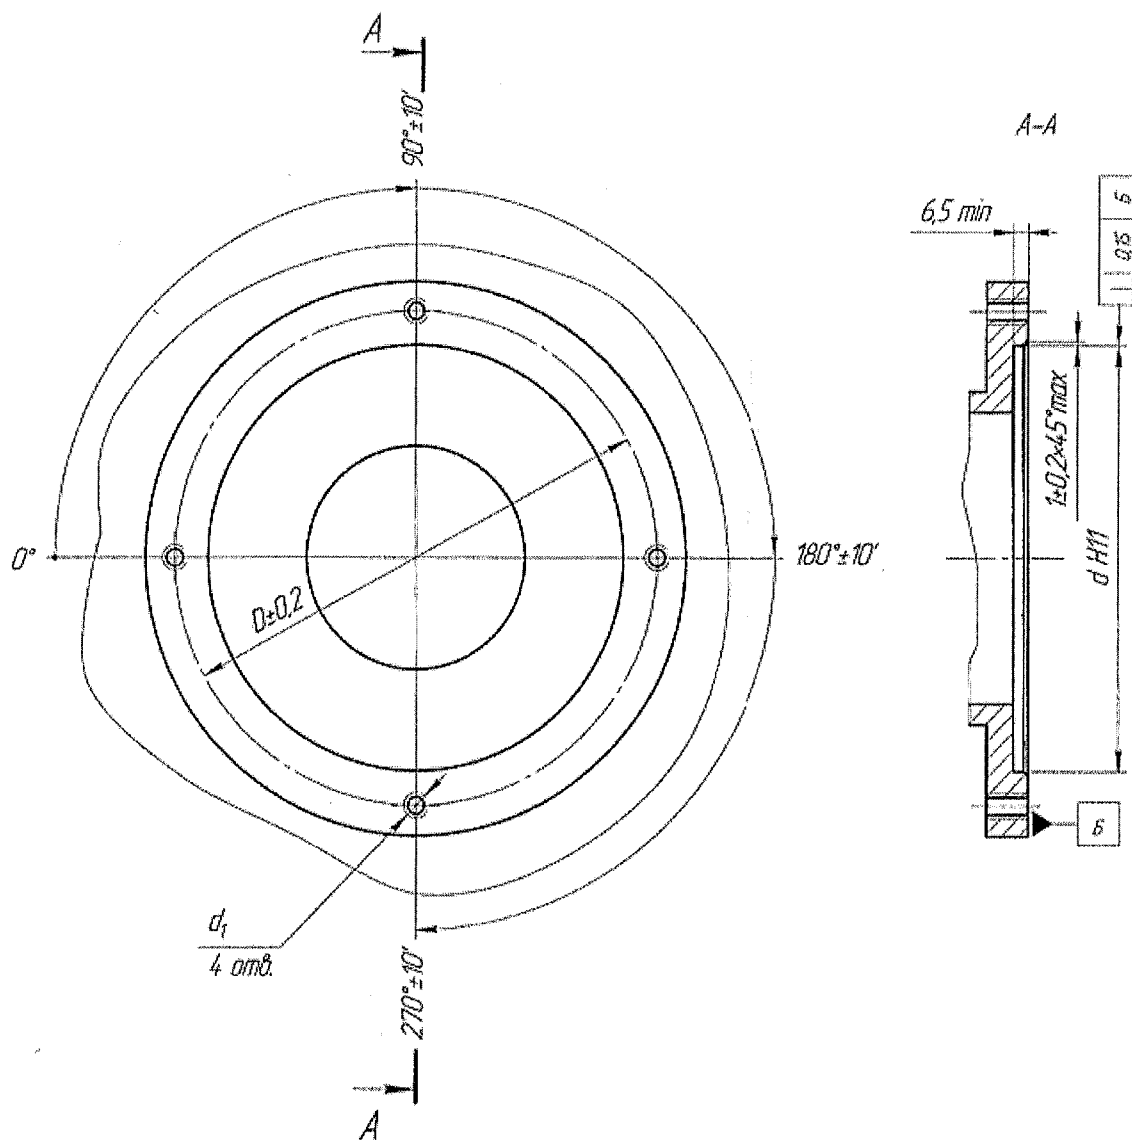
Разметка для крепления датчиков ДПС
